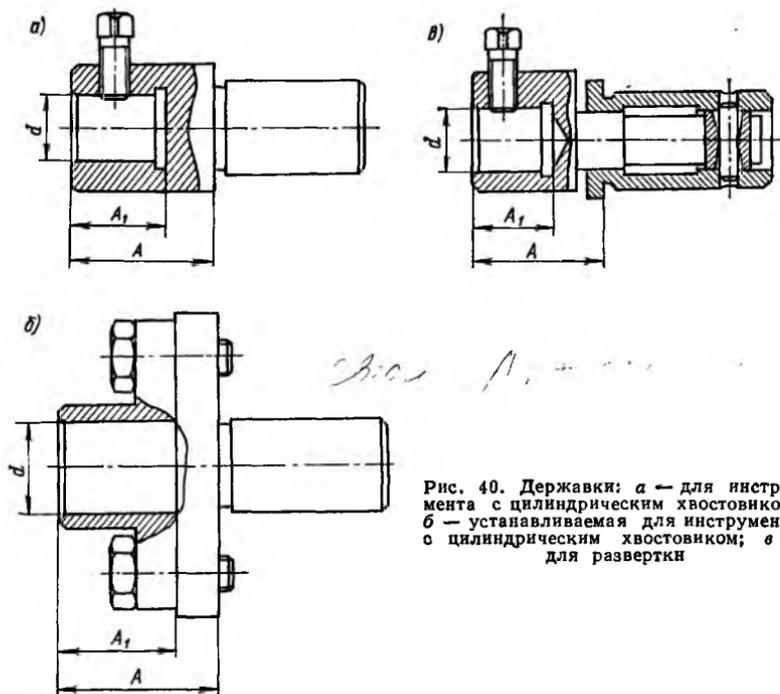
Державки: а — для инструмента с цилиндрическим хвостовиком; б — устанавливаемая для инструмента с цилиндрическим хвостовиком; в — для развертки
